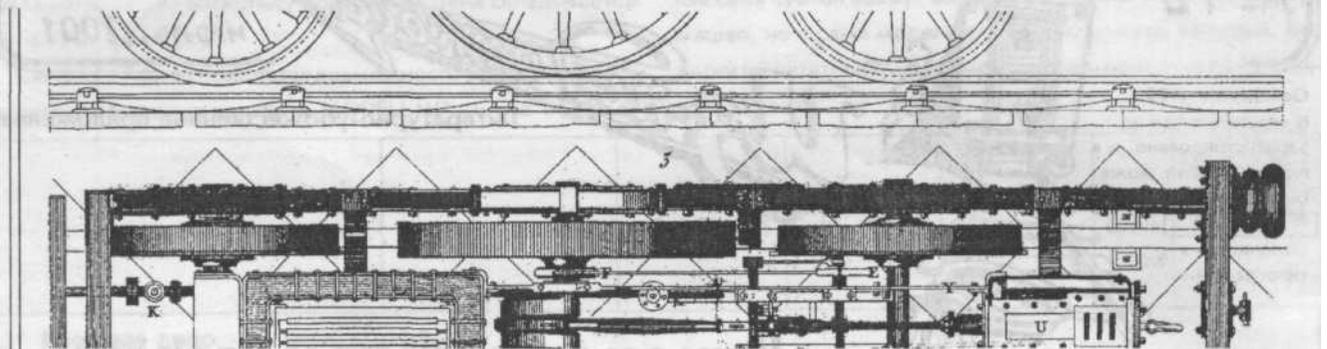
Верхний фрагмент чертежа — "взгляд" из под котла. Фрагмент внизу - разрез сверху.
